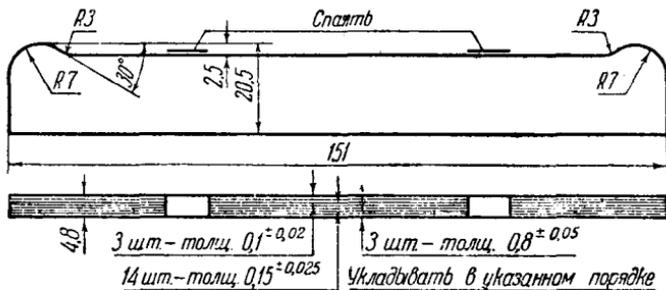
Дет. № 0319. Прокладка среднего коренного подшипника регулировочная
